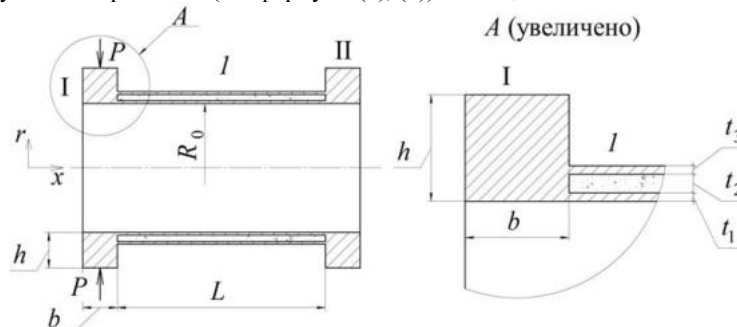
Схема трёхслойной с лёгким заполнителем стеклопластиковой цилиндрической оболочки с двумя торцевыми шпангоутами
